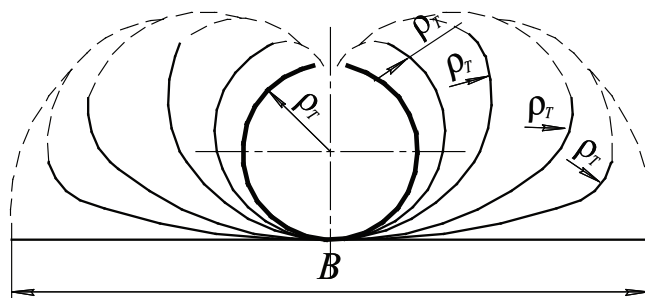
«Цветок» формовки для двухрадиусной калибровки
